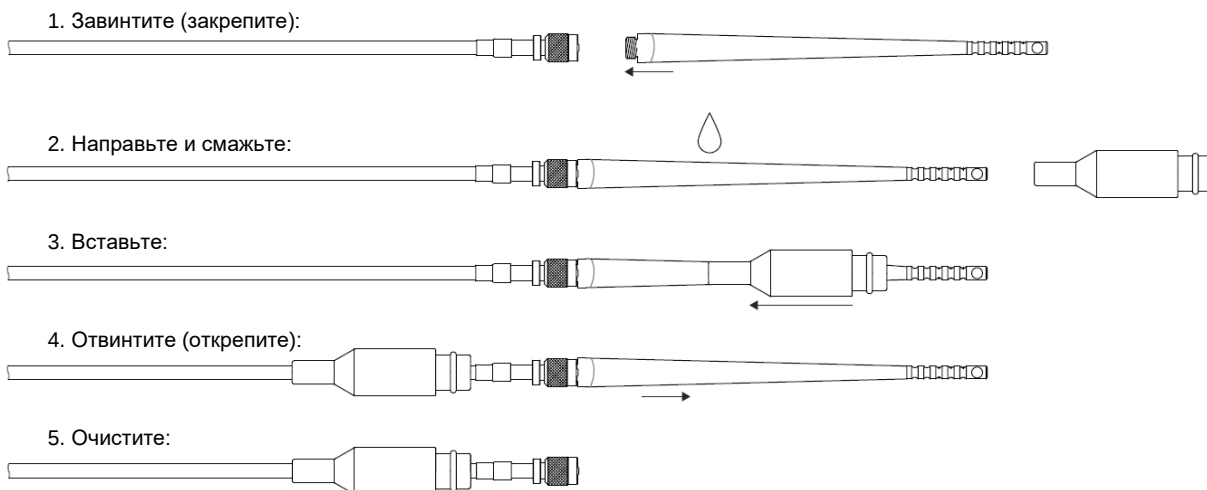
Сборка защиты межсоединений IP172 для неразъемного кабеля датчика TQ9xx
